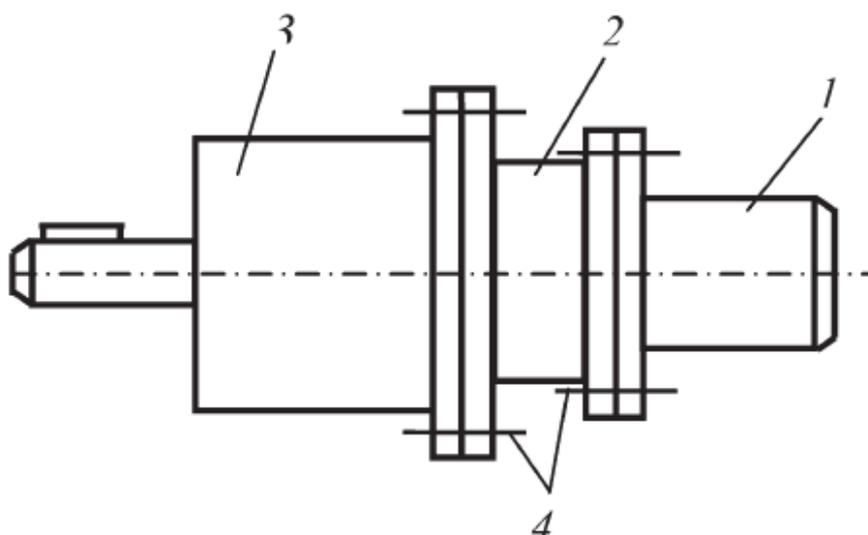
Компоновка мотор-вариатор-редуктора
